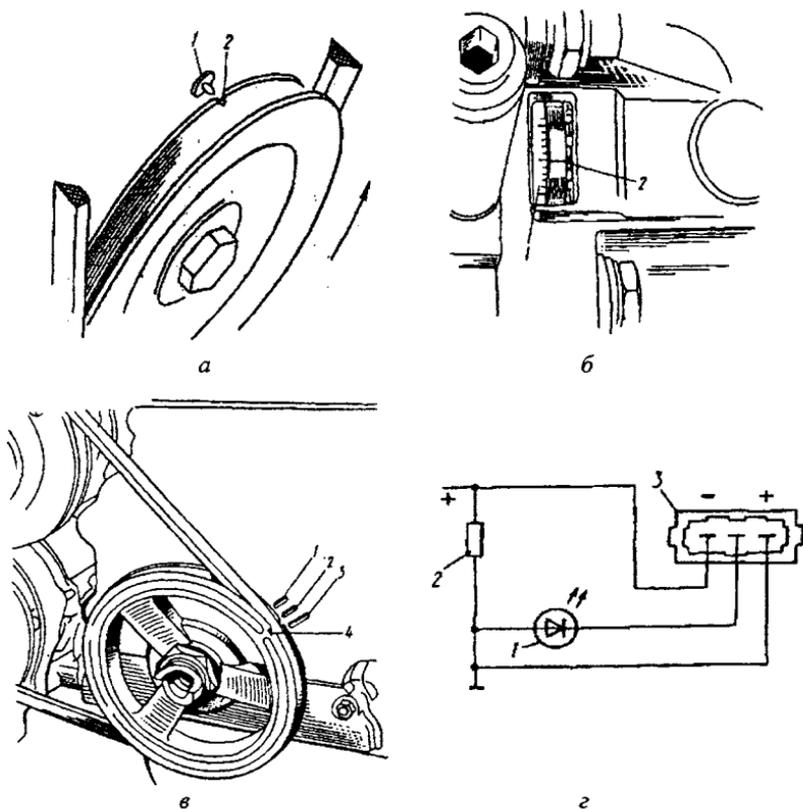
а – метка на маховике; б – шкала на картере сцепления; в – метки на корпусе двигателя – метка на шкиве; г – схема подключения индикатора для установки зажигания: 1 – светодиод АЛ307Б; 2 – резистор с сопротивлением 5 кОм; 3 – трехклеммная колодка, присоединенная к датчику Холла
